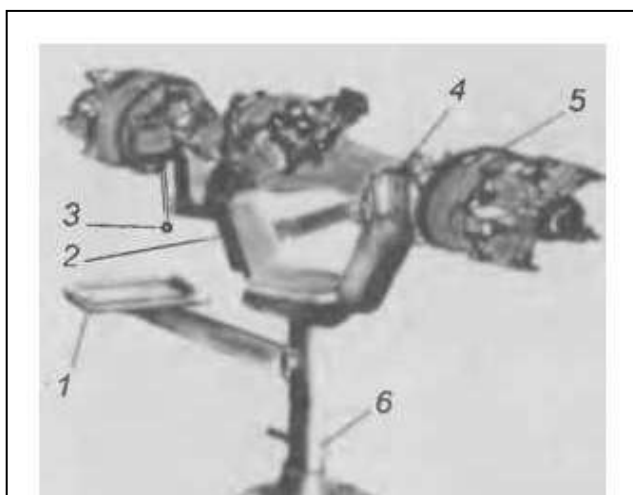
Стенд для разборки и сборки мостов автомобиля: / — подставка для сборочных единиц; 2 — ложемент; 3 — рукоять крепления моста; 4 — фиксатор; 5 — мост автомобиля; 6 — стойка
